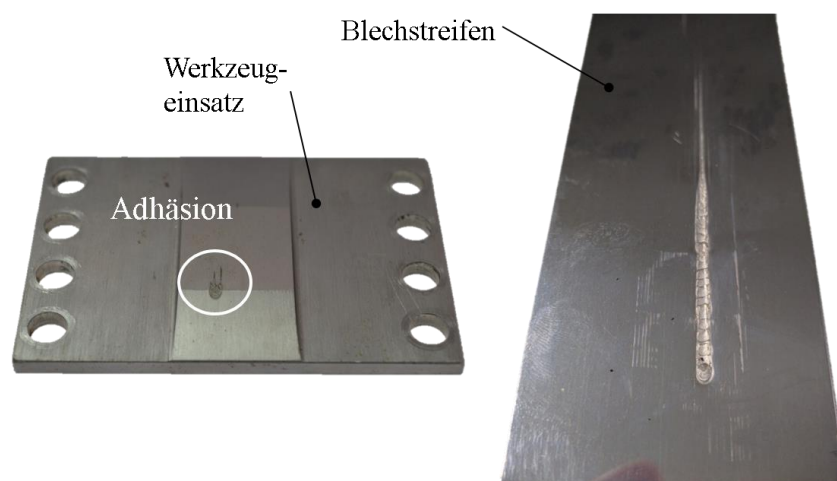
Adhäsion auf dem Werkzeugeinsatz (links) führt zu abrasivem Verschleiß am Werkstück (rechts).
